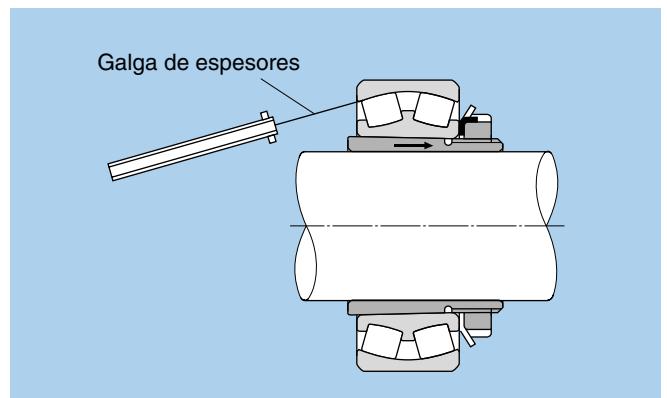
Método de medición del juego interno para rodamientos de rodillos esféricos
